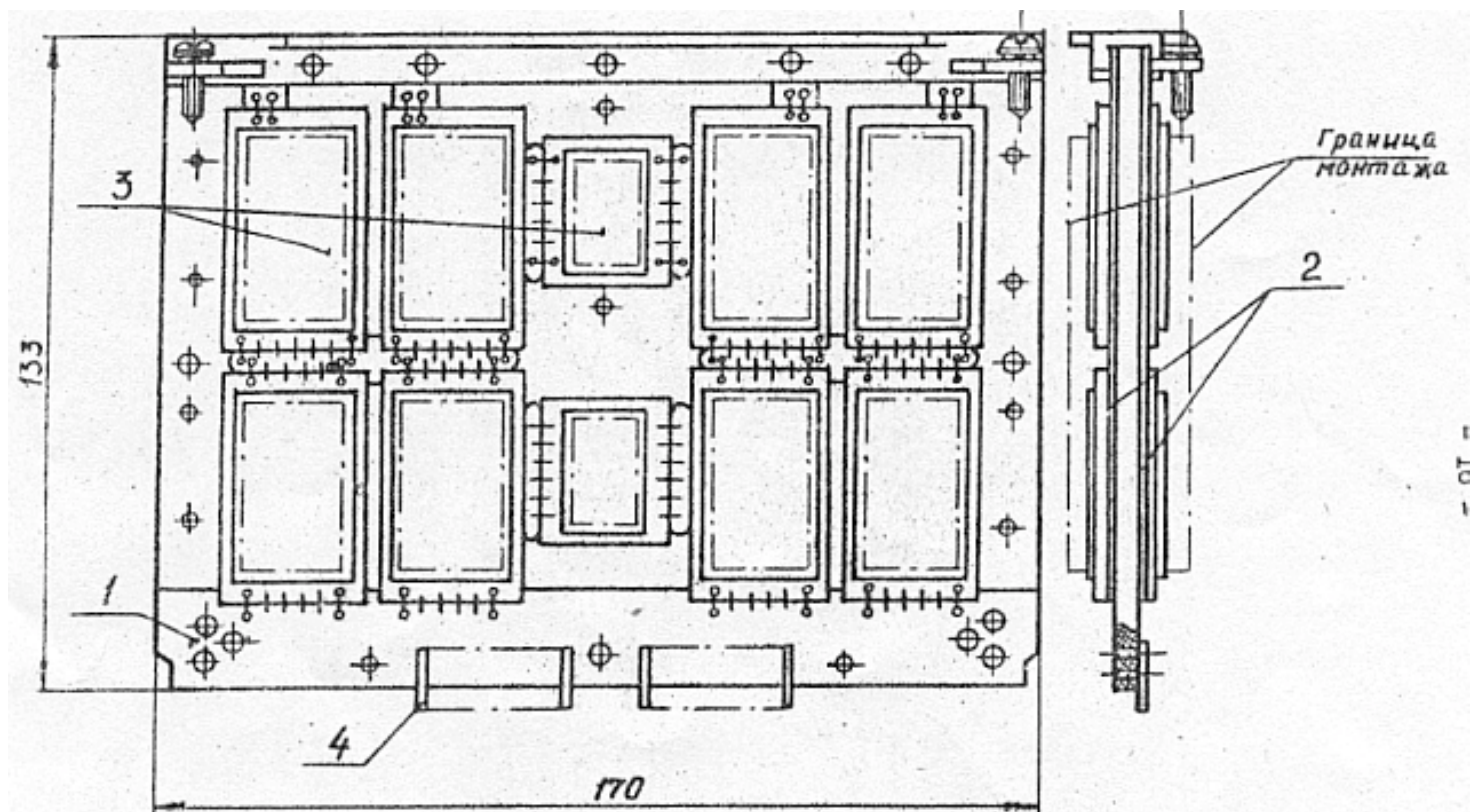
Ячейка герметичного блока разъемной конструкции: 1 - плата печатная; 2 - шина металлическая; 3 - микросборка бескорпусная; 4 - контакт разъема
